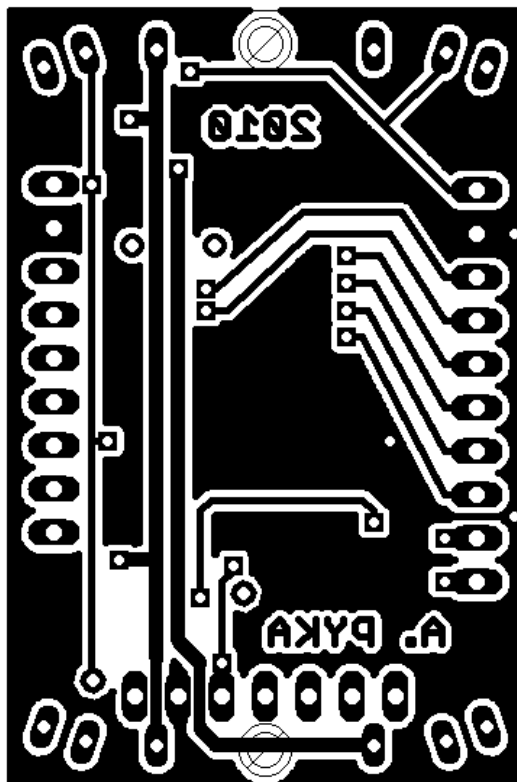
PCB modułu czujników linii – warstwa dolna
